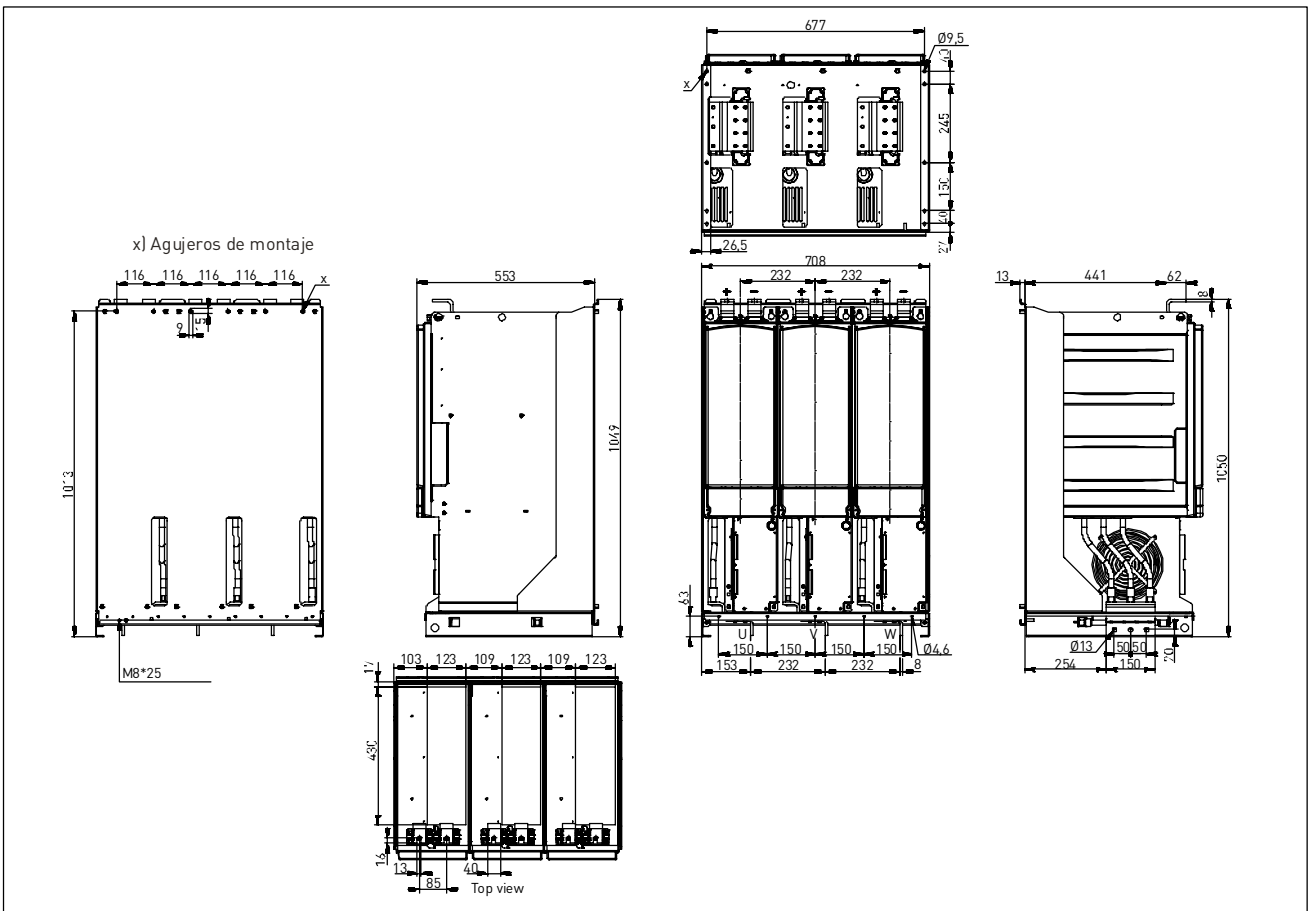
Plano dimensional, unidad inversora (FR13/14)
